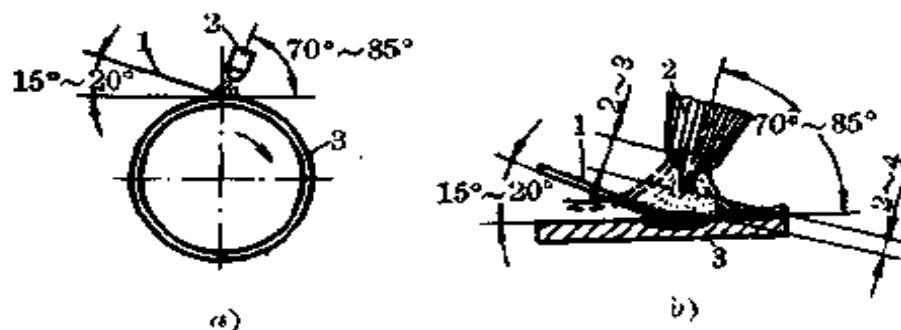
手工钨极氩弧焊焊枪、焊丝及工件的位置
